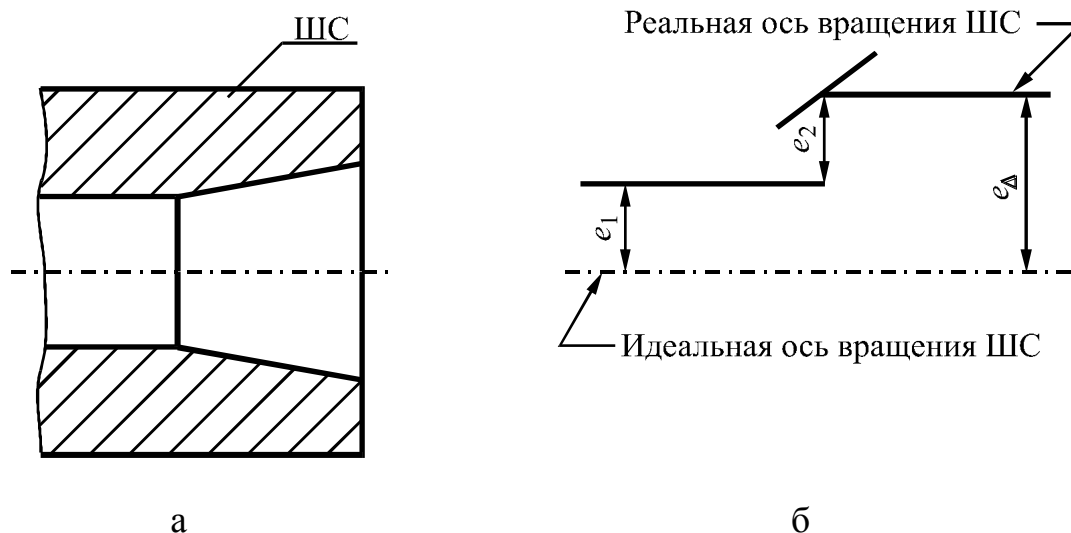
Схема размерной цепи погрешностей, влияющих на биение оси вращения шпинделя станка (ШС): а – гнездо ШС для установки инструментальных блоков; б – размерная цепь погрешностей расположения оси ШС
